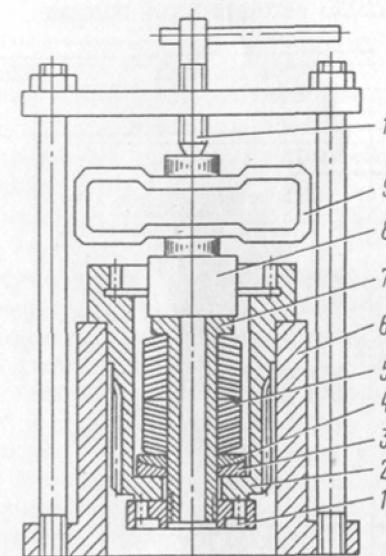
Сборочный узел для предварительного нагружения пакета тарельчатых пружин
